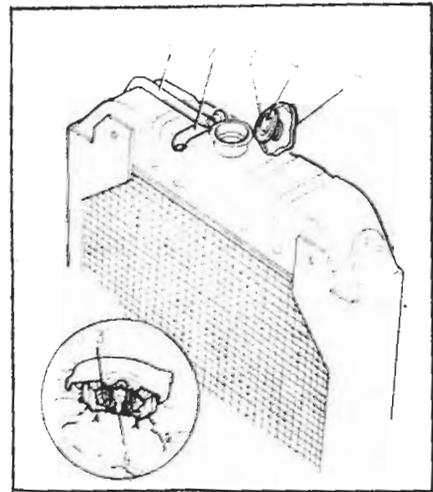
Radiador. 1.- Tubo de rebose. 2.- Tubo del cable de mando de la cortinilla delantera. 3.- Muelle de válvula. 4.- Disco de válvula. 5.- Cierre manual del tapón.
